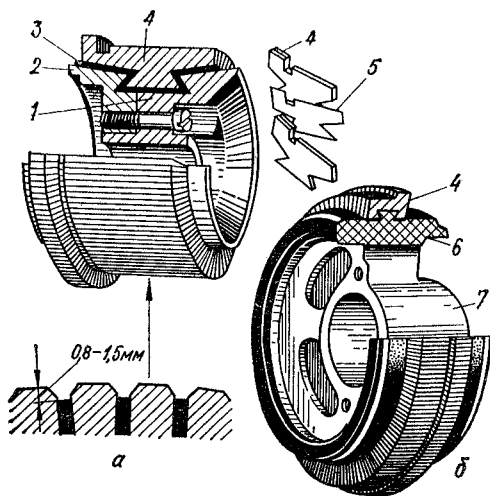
Колектори з металічним (а) і пластмасовим (б) корпусами.
